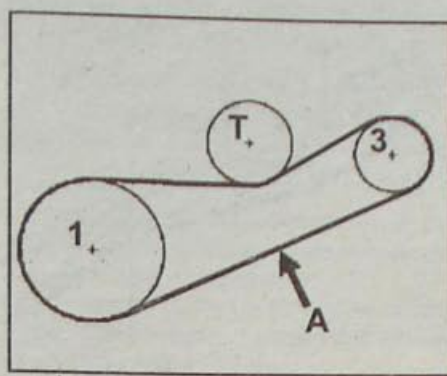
Расположение на шкивах ремня привода вспомогательного оборудования двигателя Z:
